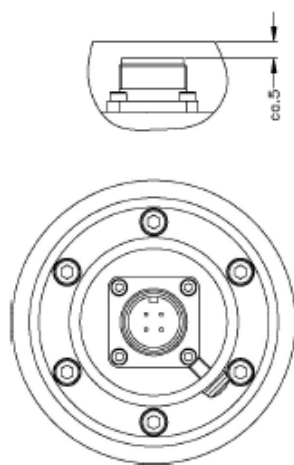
Габаритные размеры датчика HU 300, стандартное исполнение.
